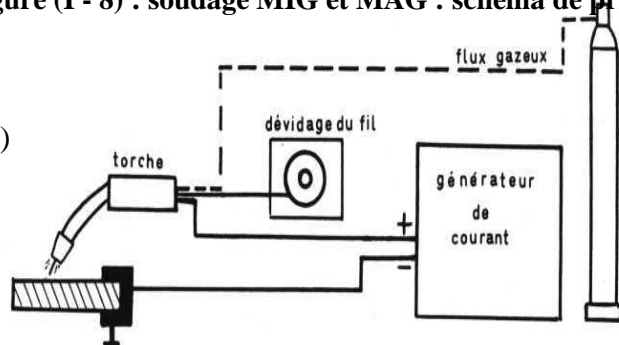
soudage MIG et MAG : schéma de l'installation [10] .
